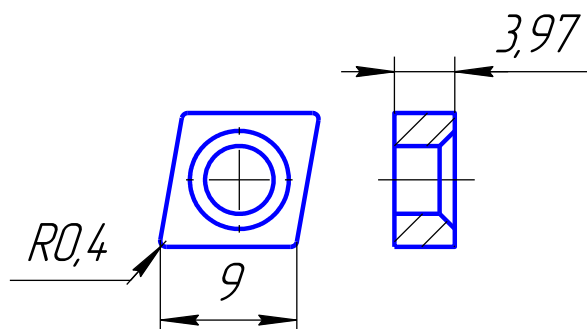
Форма і розміри обраної пластини для чистової обробки деталі
